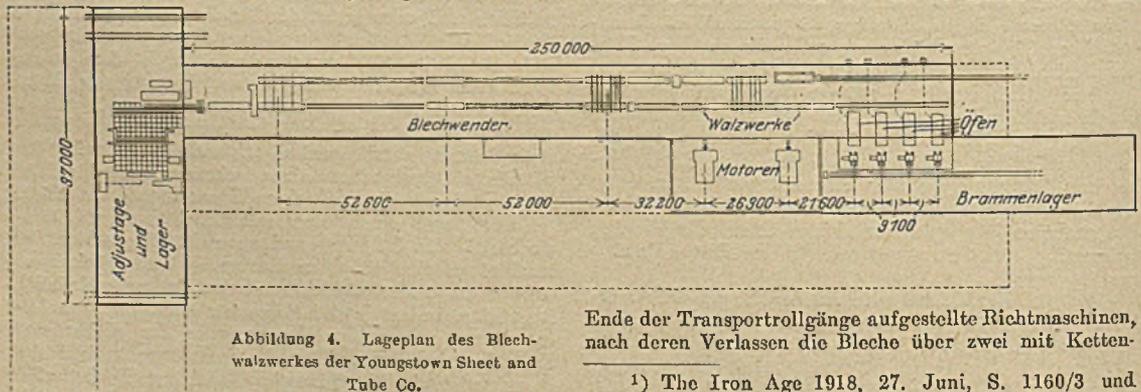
Lageplan des Blechwalzwerkes der Youngstown Sheet and Tube Co.
